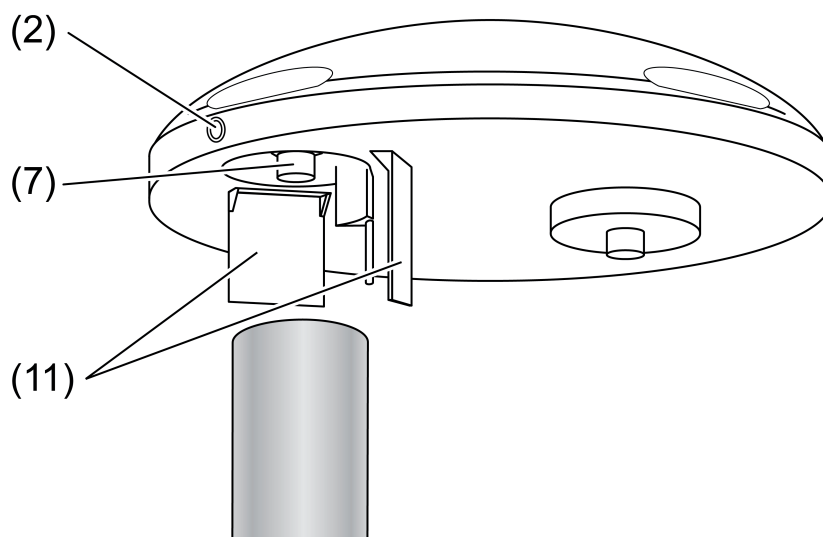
Монтаж на отдельно стоящем столбе без крепежного кронштейна
